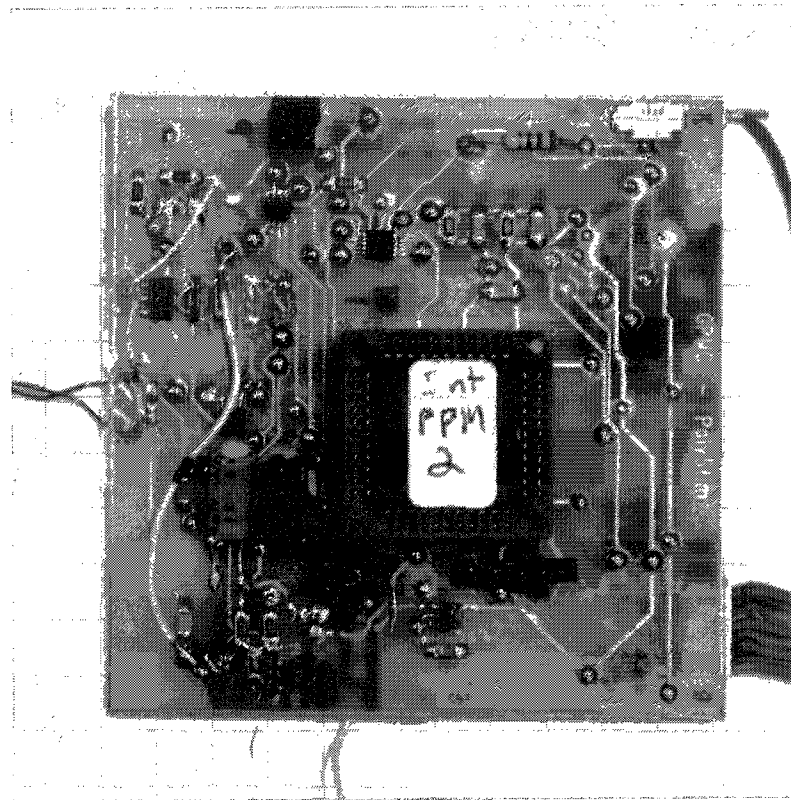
Photographie du circuit assemblé, vue de dessus
